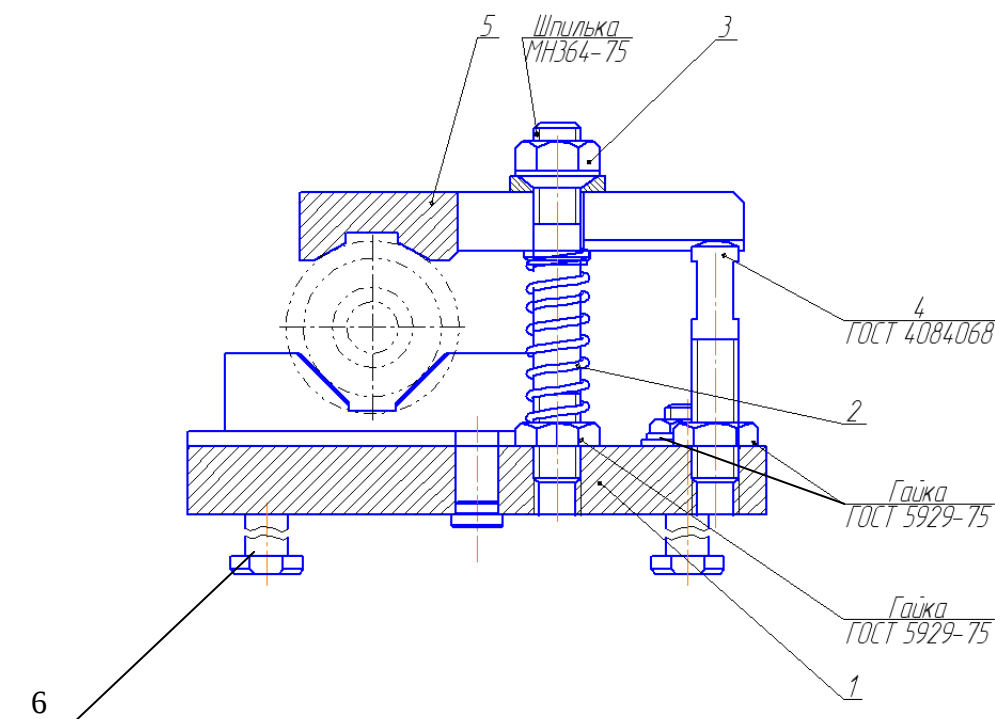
Приспособления для зажима вала на фрезерной операции по фрезерованию шпоночного паза.
